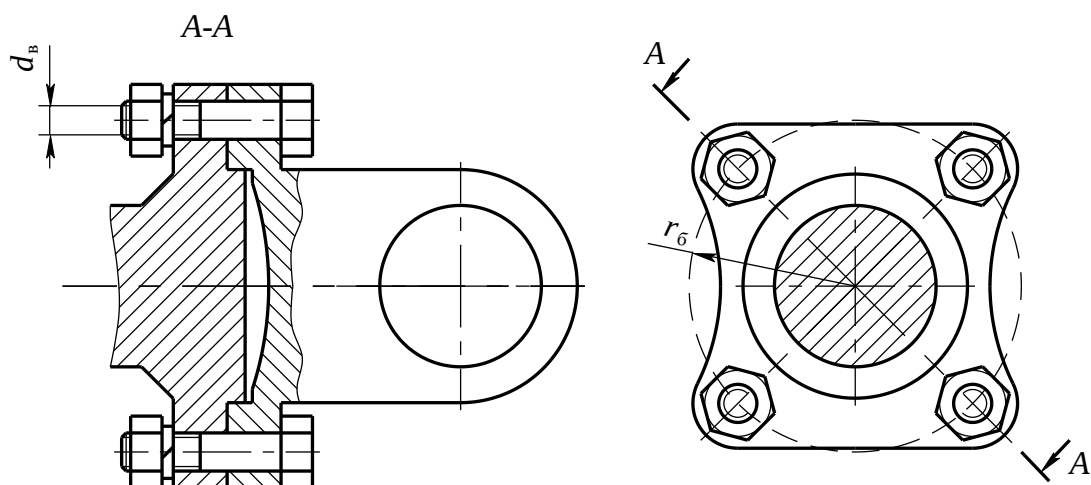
Схема фланцевого з'єднання вала та вилки
